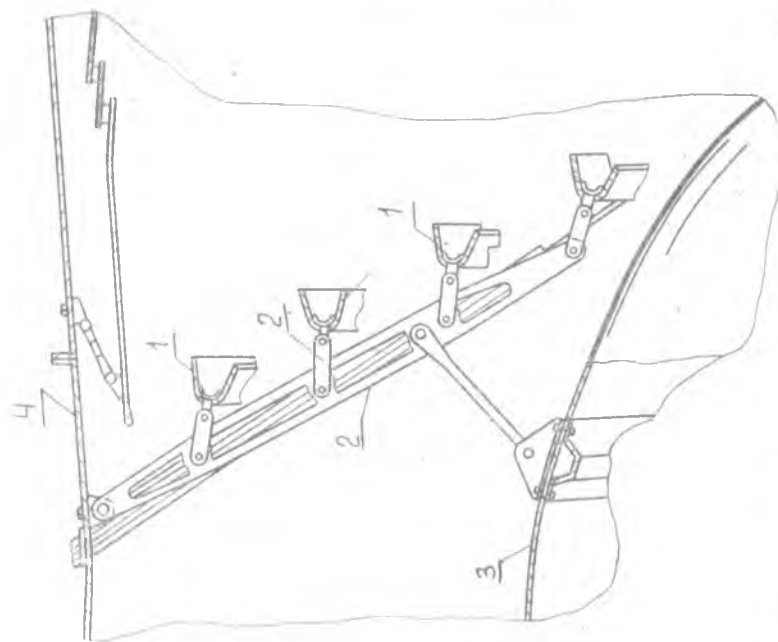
Форсажная камера: 1 — стабилизаторы; 2 — детали крепления стабилизаторов; 3 — стекатель; 4 — корпус камеры
